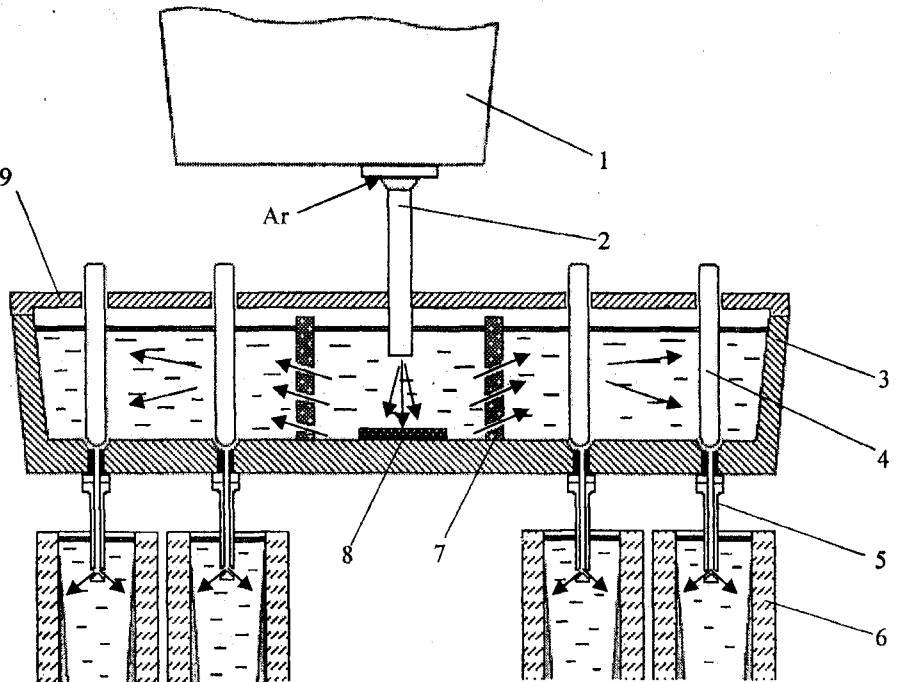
Схема разливки металла из сталеразливочного ковша через промежуточный ковш в кристаллизаторы: 1 – сталеразливочный ковш; 2 – защитная труба (воронка); 3 – промежуточный ковш; 4 стопор; 5 – погружной стакан; 6 – кристаллизатор; 7 – перегородка; 8 – “бойное” место; 9 – крышка ковша
